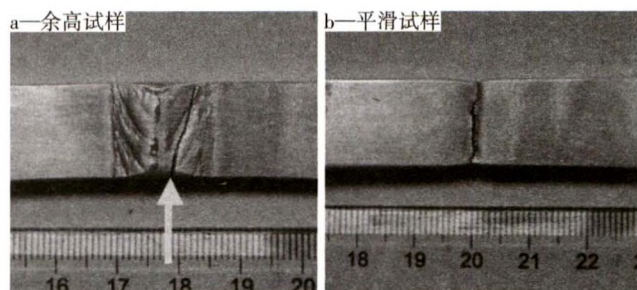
铝合金焊接接头疲劳断裂宏观形貌
